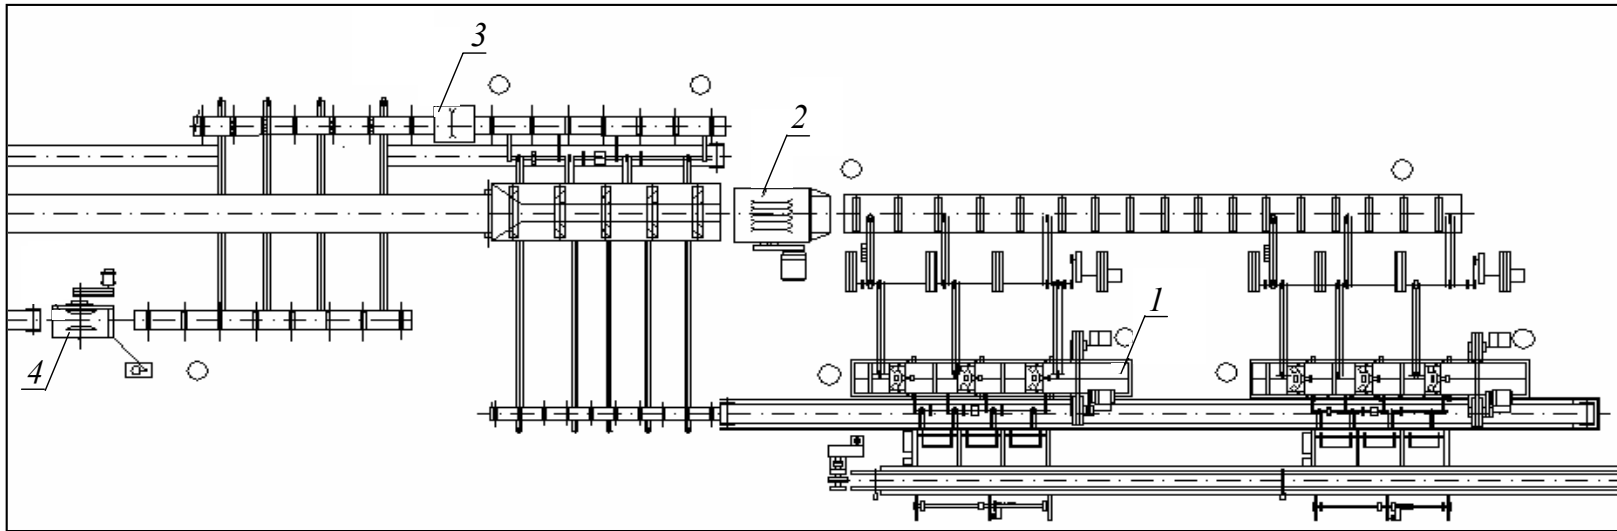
Схема расположения оборудования в цехе на базе горизонтальных ленточнопильных и круглопильного станков:
